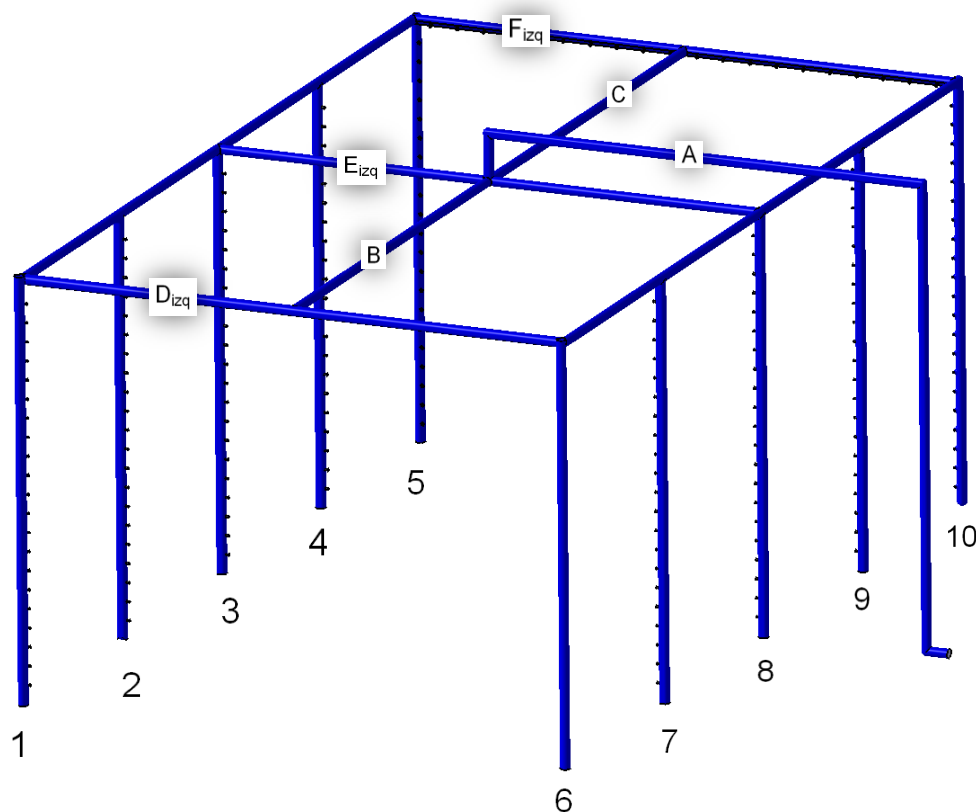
Estructura de tuberías con etiquetas para el cálculo de los tramos.
